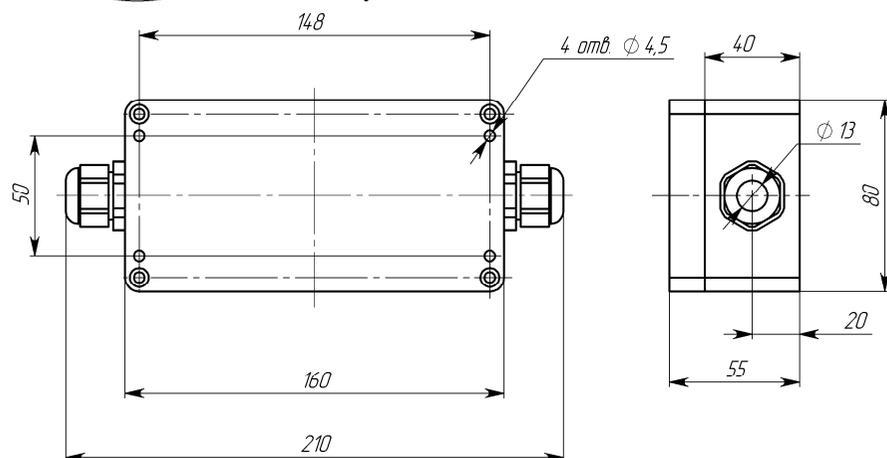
Габаритные размеры устройства управления оповещателем УУО.
